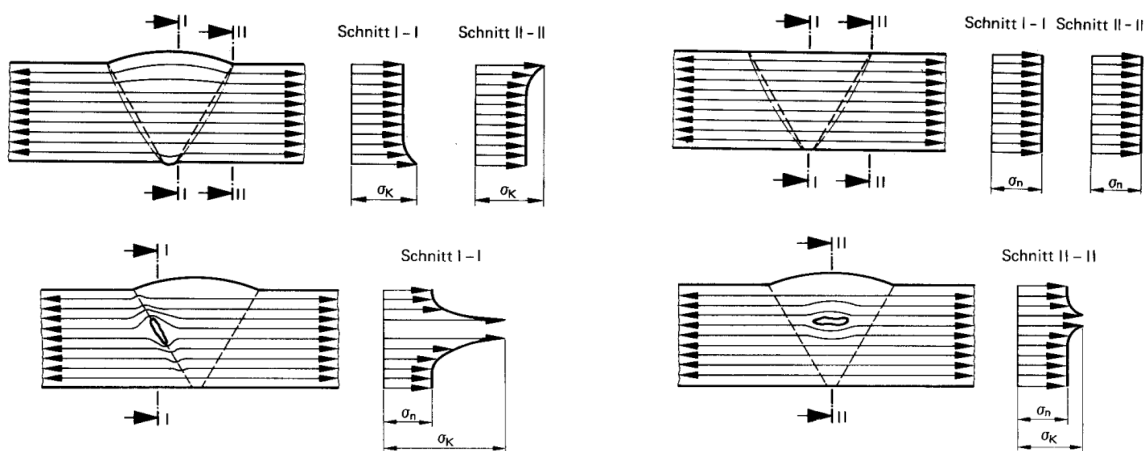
Spannungsverteilung in einer fachgerecht geschweißten Stumpfnaht (links oben) sowie in einer blecheben bearbeiteten Stumpfnaht (rechts oben), Stumpfnaht mit einem Bindefehler quer zur Beanspruchungsrichtung (links unten) sowie mit einem Bindefehler in Beanspruchungsrichtung (rechts unten) [Scheermann 1997]
